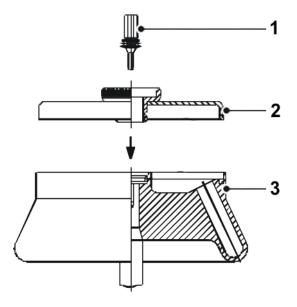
Rotor angulaire standard avec couvercle hermétique
